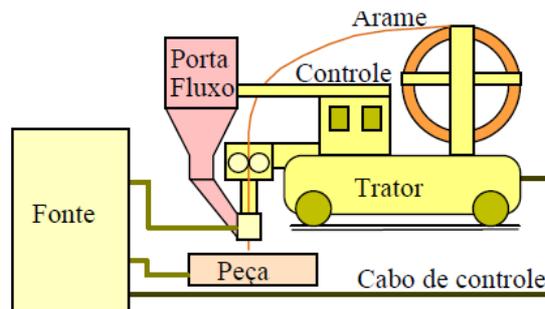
Ilustração de um equipamento utilizado na soldagem.
